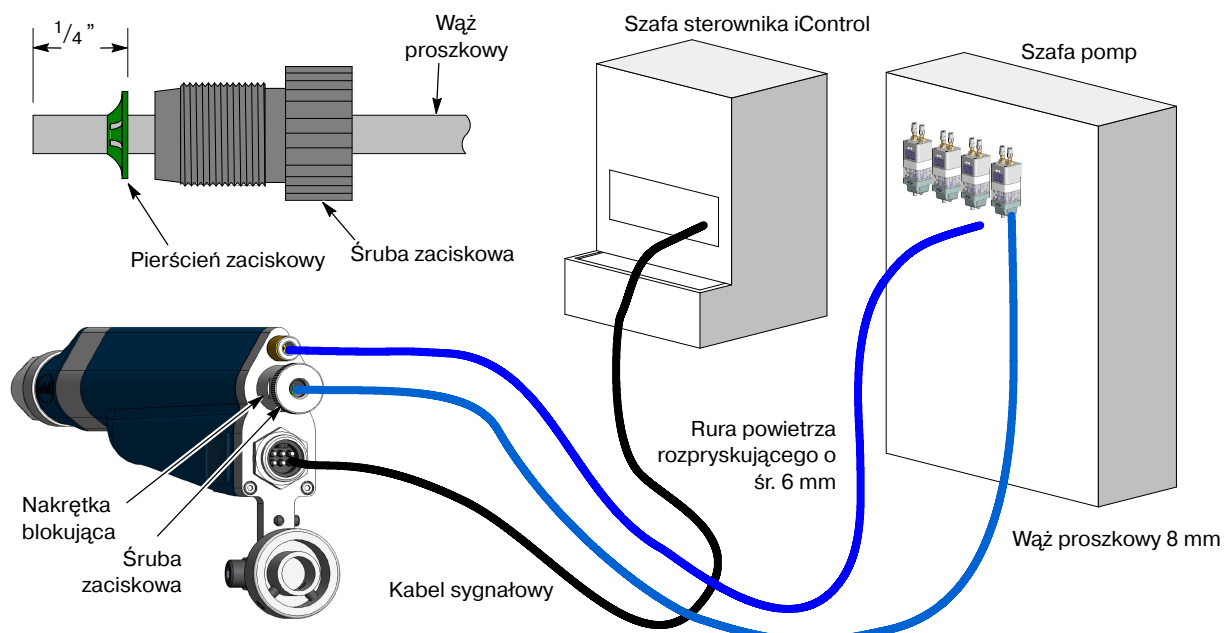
Montaż pistoletu mocowanego na pręcie.
